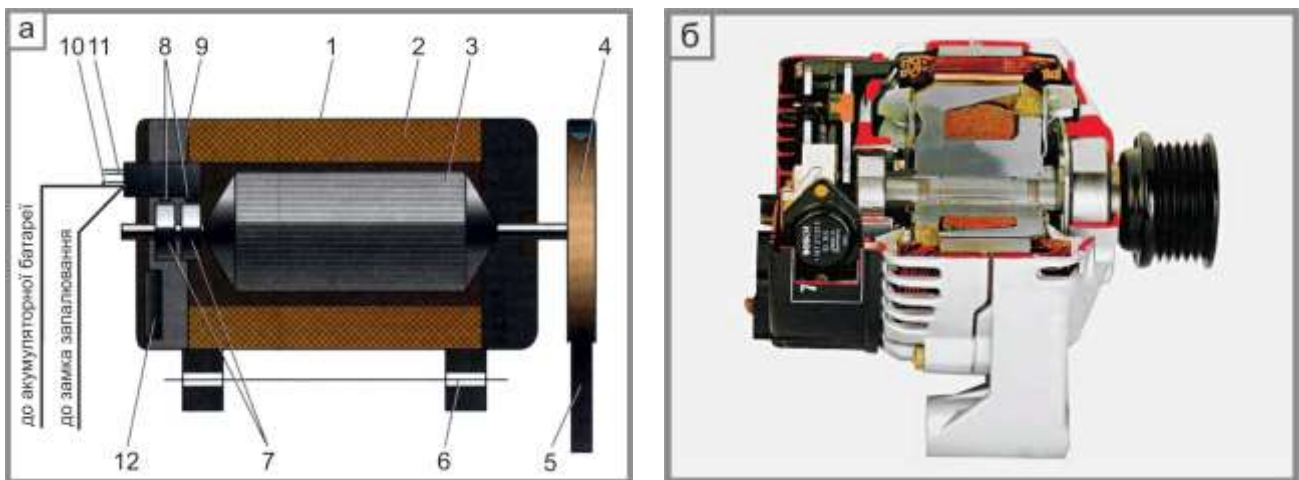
Пристрій (а) і загальний вид (б) генератора: 1 – корпус генератора; 2 – обмотка статора; 3 – ротор; 4 – шків приводу генератора; 5 – пас; 6 – кронштейн кріплення; 7 – контактні кільця; 8 – щітки; 9 – регулятор напруги; 10 – вивід «30» для підключення споживачів; 11 – вивід «61» для живлення ланцюга амперметра і контрольних ламп на щитку приладів; 12 – випрямляч
